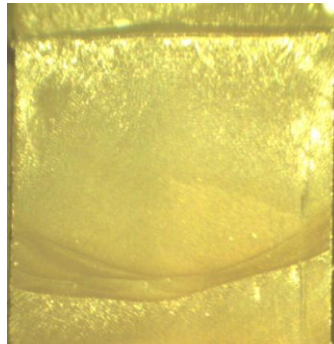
Superficie de fractura de una probeta del ensayo 10.
